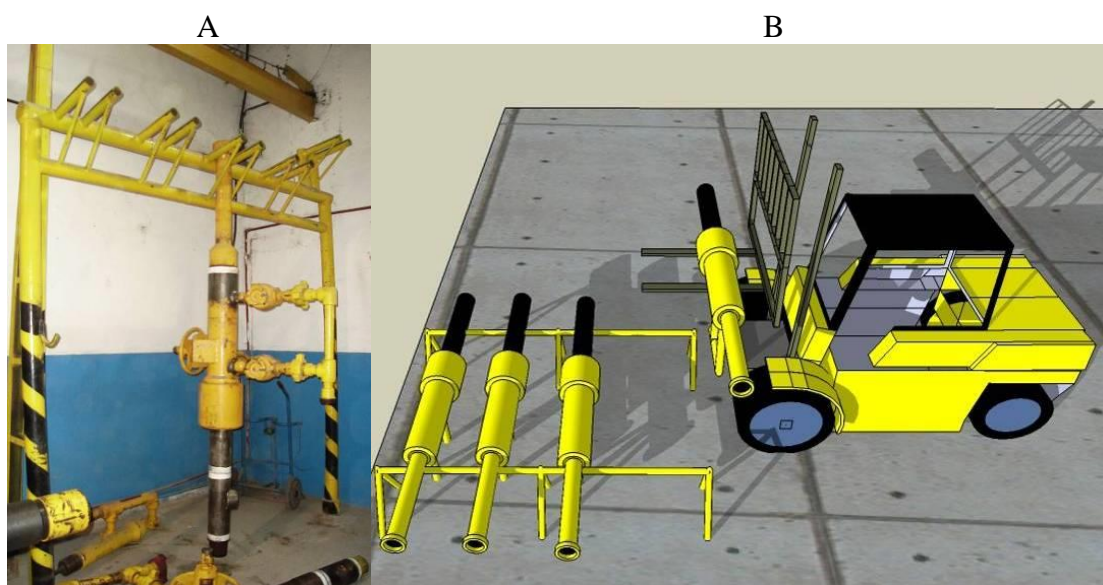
A) Rack Vertical existente en la base actual. B) Colocación sobre caballetes
